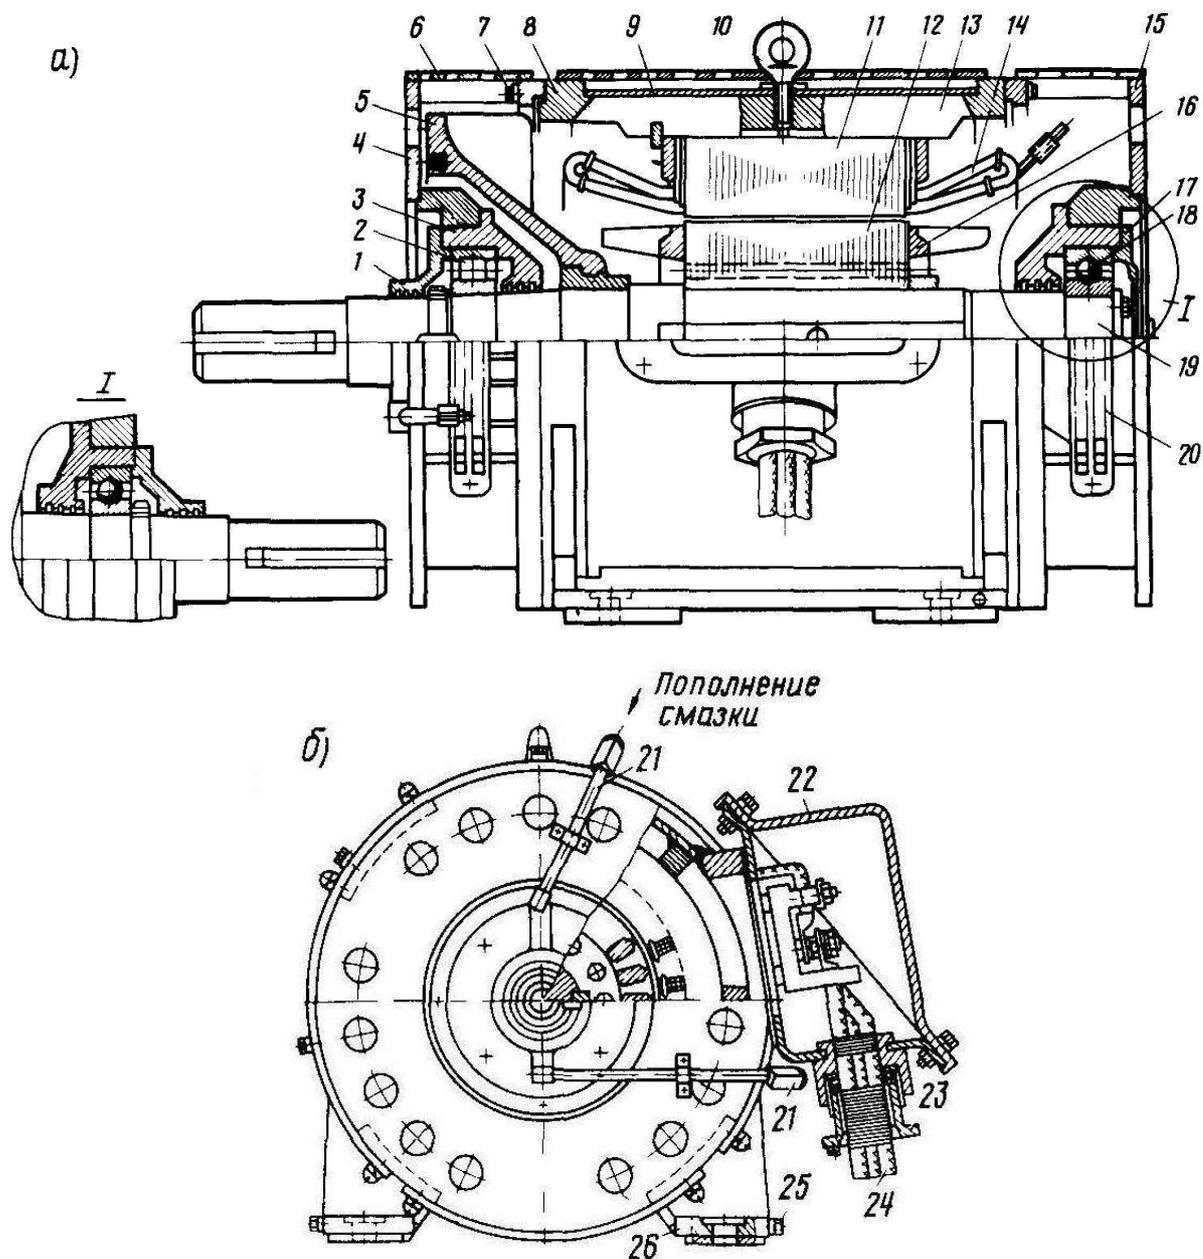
Продольный (а) и поперечный (б) разрезы электродвигателя АЭ92-402: 1 - крышка лабиринтная; 2, 18 - подшипники; 3 - капсуля подшипника; 4, 15 - подшипниковые щиты; 5 - вентилятор; 6, 20 - сетки; 7 - болт; 8 - кольцо стопорное; 9 - обшивка станины; 10 - болт грузовой; 11, 12 - сердечники статора и ротора соответственно; 13 - ребро станины; 14 - обмотка статора; 16 - клетка ротора; 17 - крышка подшипника; 19 - вал; 21 - маслопровод; 22 - коробка выводов; 23 - гайка сальника; 24 - провод; 25 — болт заземления; 26 — лапа станины
